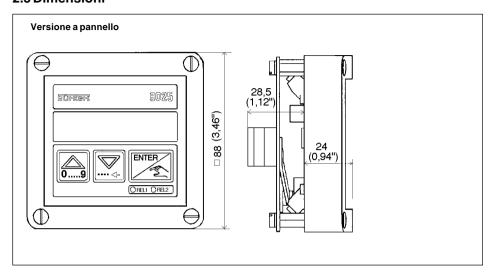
Dimensioni Trasmettitore 8025 versione a pannello
